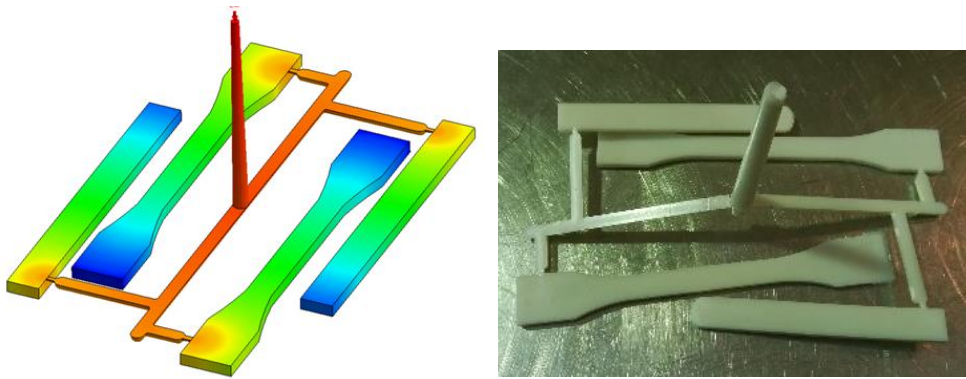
a) Diferença entre moldação por CAE e b) moldações reais obtidas
